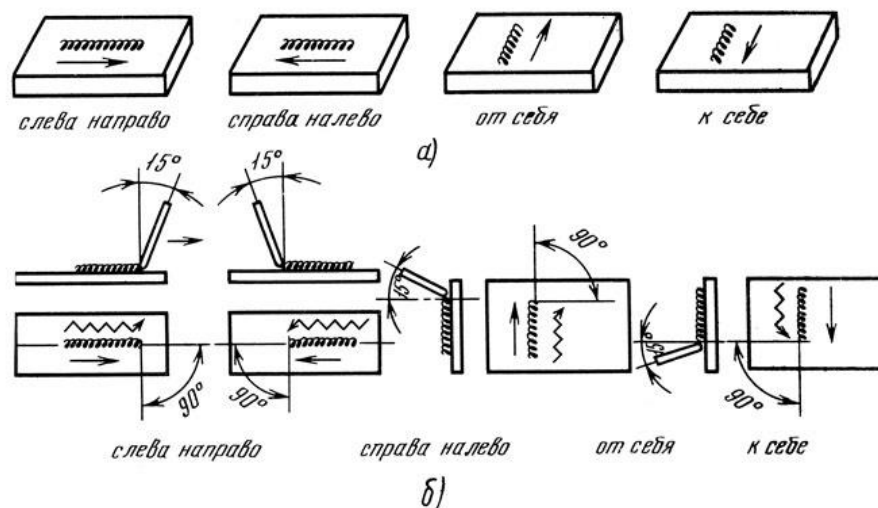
Направления сварки (а) и наклон электрода (б)
